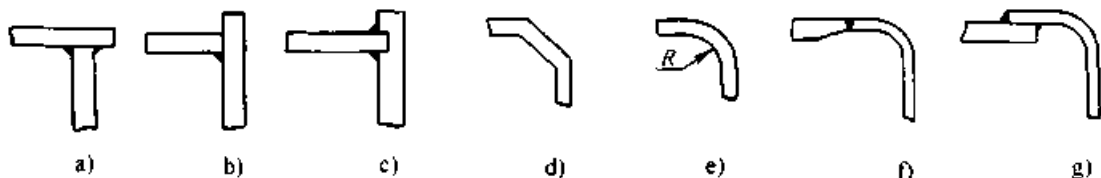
焊接开式机架喉口转角处内侧板的结构形式
